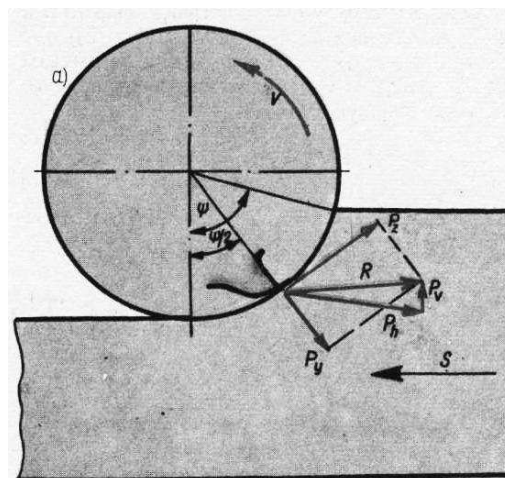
Схема сил різання при зустрічному фрезеруванні.
